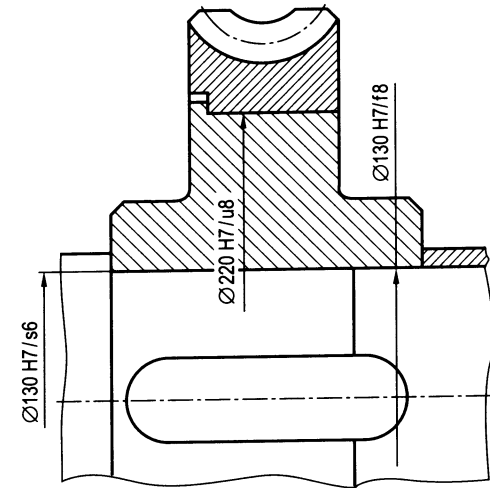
Соединение центра червячного колеса с банджом и валом
